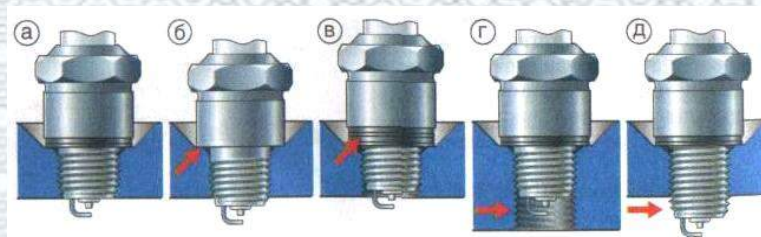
Правильні й неприпустимі способи установки свічі: а - правильна установка; б - немає ущільнювального кільця; в - два ущільнювальні кільця; г - різьбова частина коротка; д - різьбова частина довга
